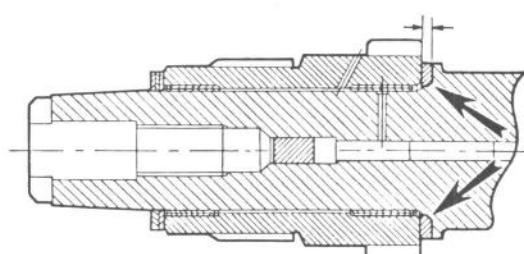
Reglaje del juego en el engranaje del cigüeñal, cuando dicho engranaje va montado sobre casquillos lubrificados por el circuito de engrase. El juego debe estar comprendido entre 0,076 y 0,152 mm.
